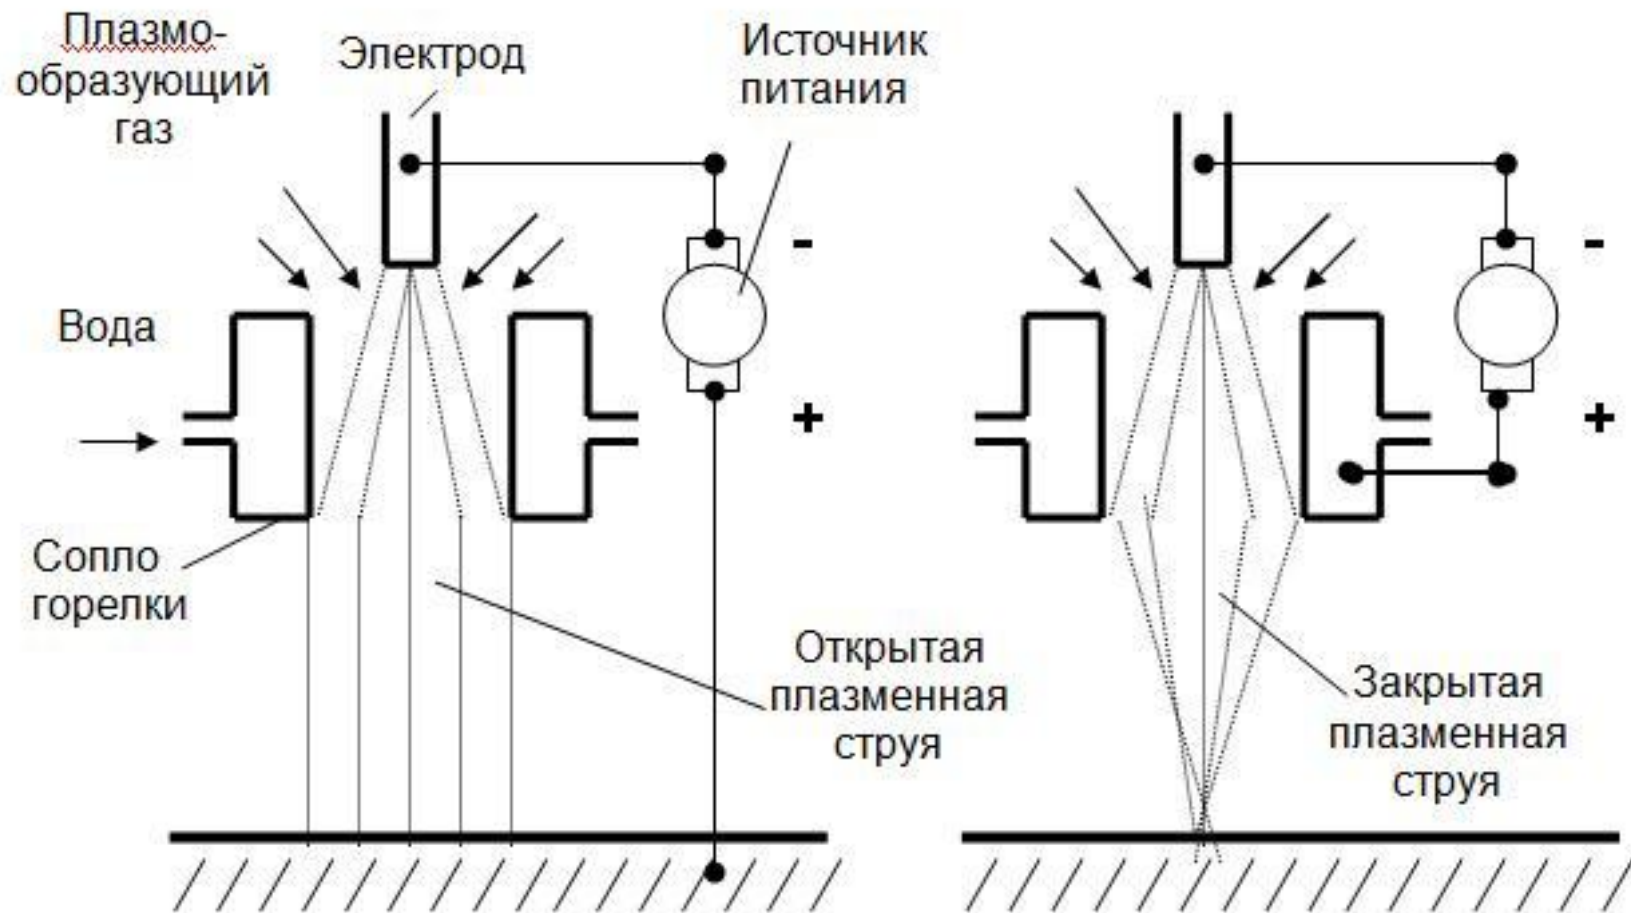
Схема плазменной сварки открытой и закрытой плазменной струей.
